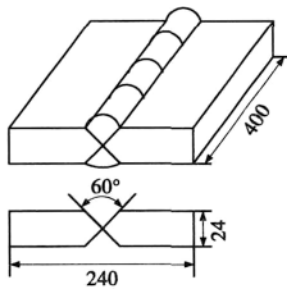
实际焊接试件尺寸及坡口形式示意图 (mm)
